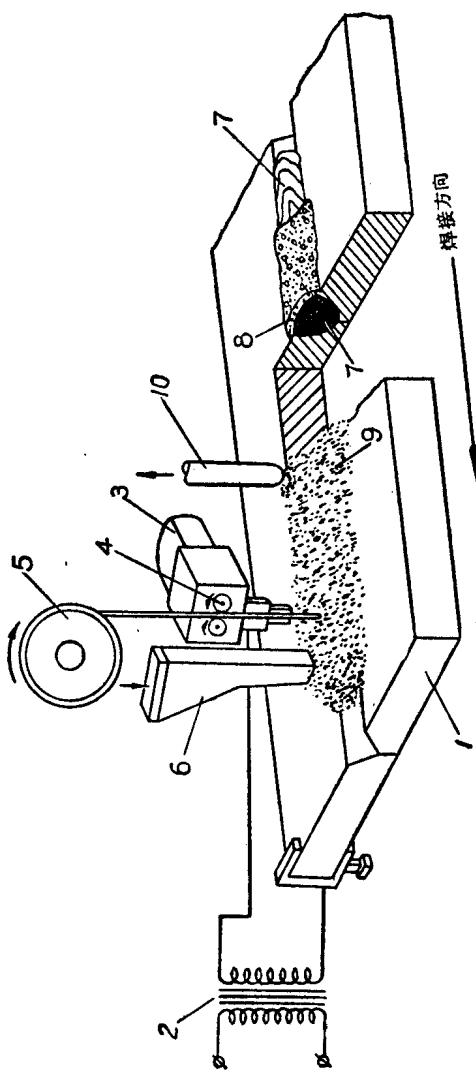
焊剂層下自動電弧焊的焊接過程：
